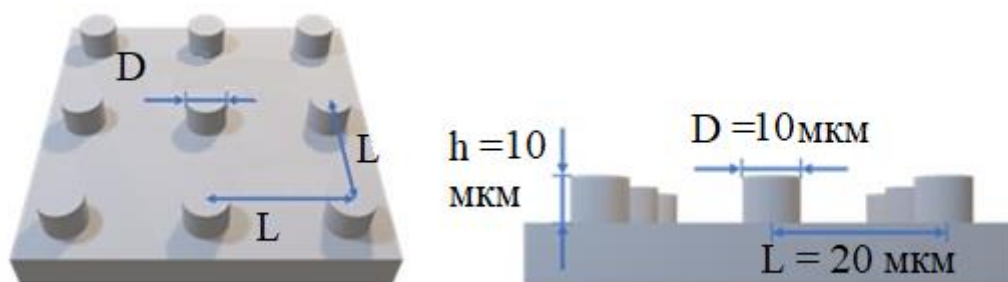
Внешний вид и размеры изделия ТЗ№1.
